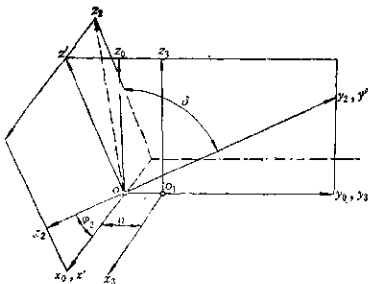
圆柱齿轮与非渐开线圆锥齿轮啮合
